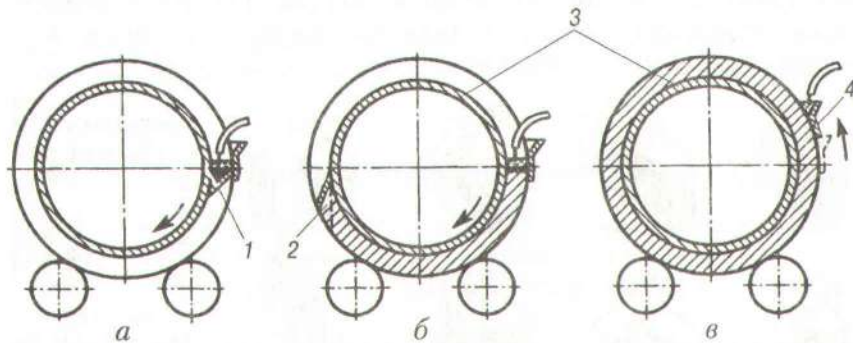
Схема електрошлакового зварювання кільцевих швів:
